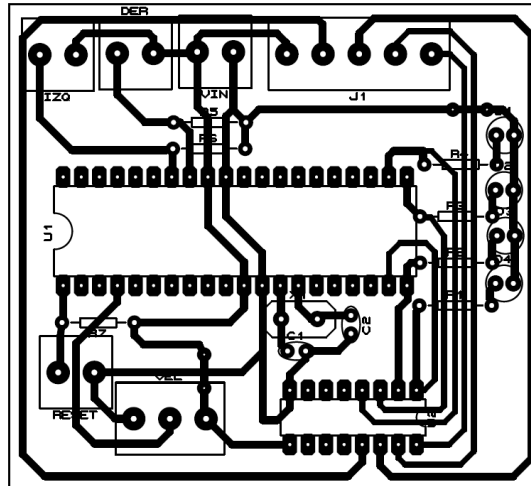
16: Tarjeta de circuito impreso de motor PaP unipolar.
